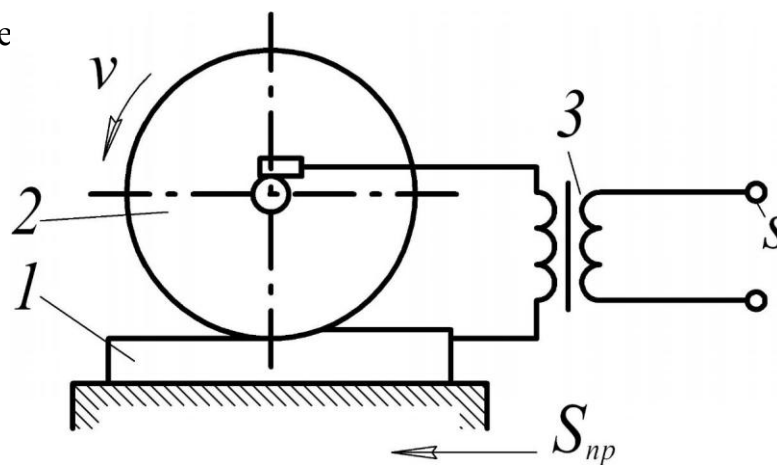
Схема електроконтактної обробки плоскої поверхні
